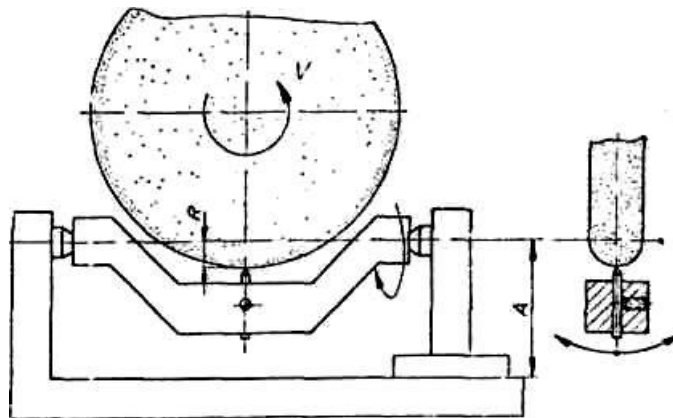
Приспособление для профилирования кругов по дуговым участкам профиля; схема приспособления
